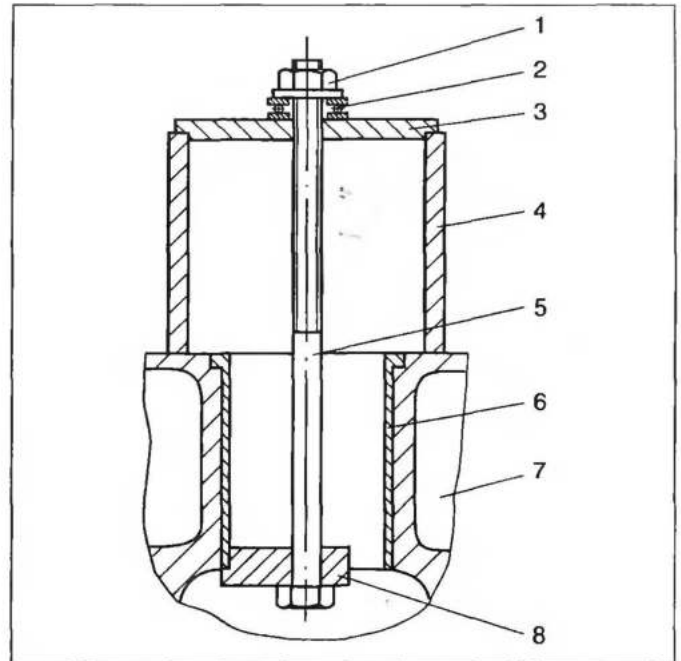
Выпрессовка "сухой" гильзы из блока цилиндров: 1 — гайка; 2 — подшипник; 3 — крышка; 4 — цилиндр; 5 — болт; 6 — гильза; 7 — блок; 8 — опора болта
